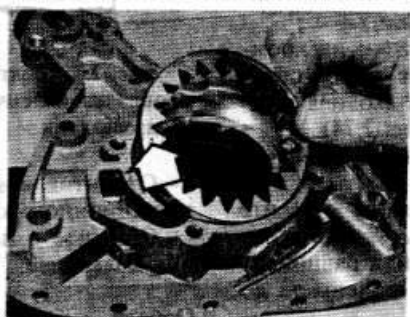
Метка (показана стрелкой) на торце шестерни
